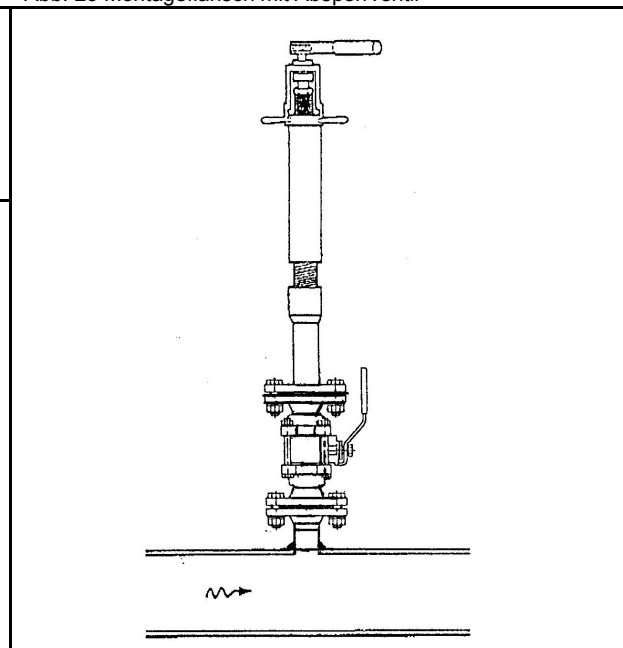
Bohrmaschine mit Flanschadapter auf Absperrventil..
